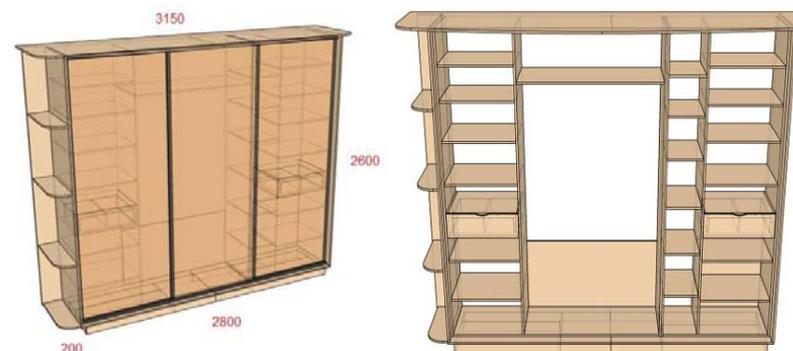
Большой гардеробный шкаф: а – внешний вид; б – внутренняя конструкция
